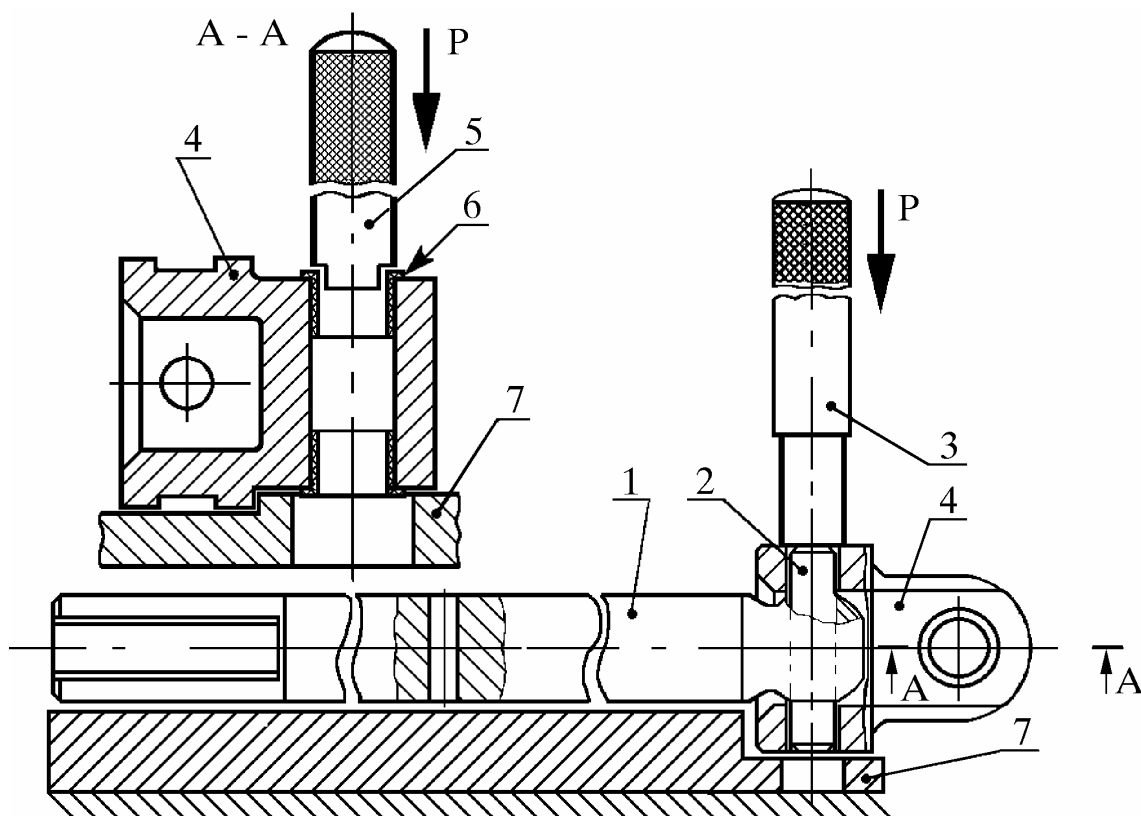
Сборка вала механизма переключения с корпусом шарнира:
